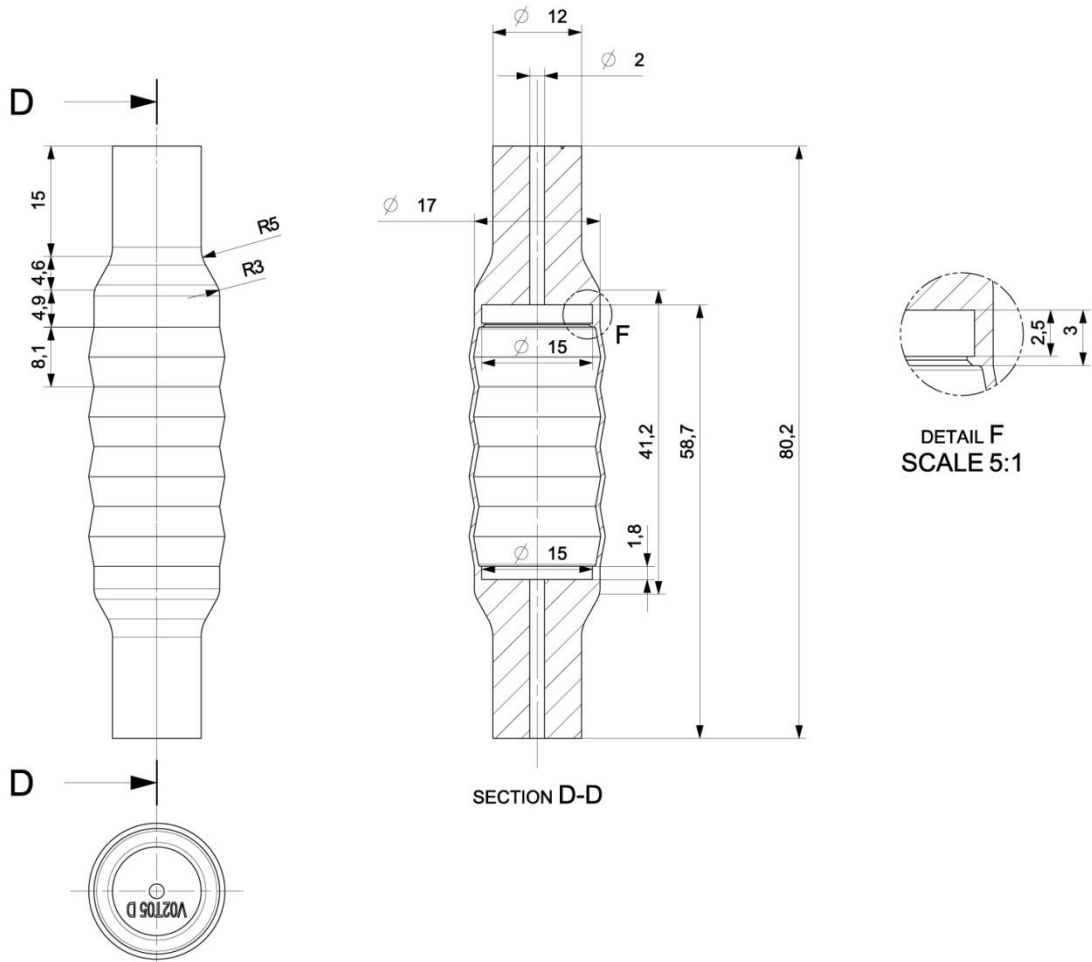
Technische Zeichnung Aktormodulgehäuse V02T05
